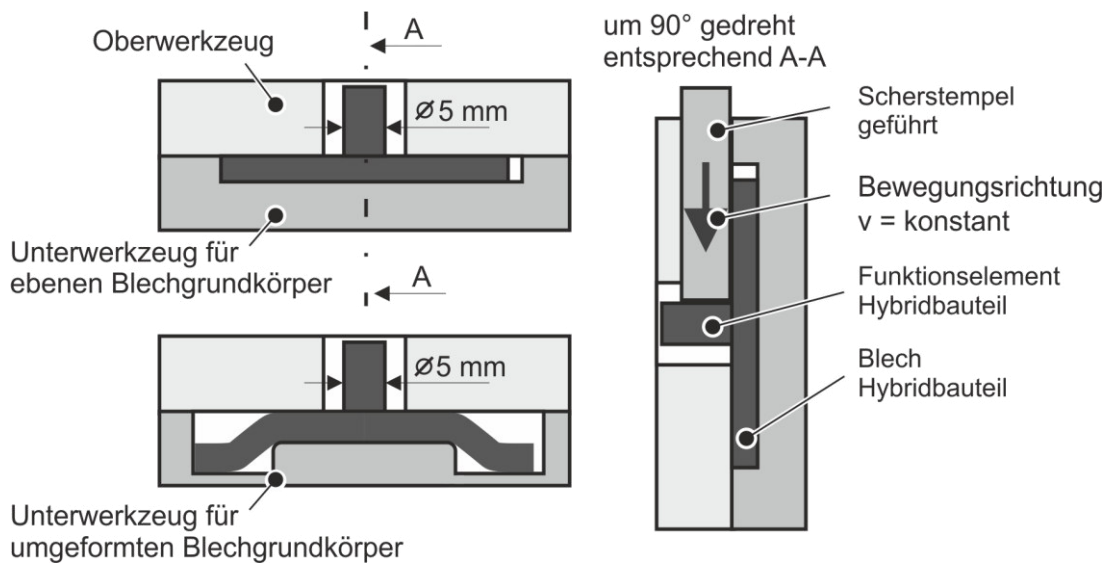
Schematischer Aufbau des Scherversuchs zur Bestimmung der Scherfestigkeit von hybrid gefertigten Bauteilen der Titanlegierung Ti-6Al-4V (a) mit Blickrichtung seitlich auf das Werkzeug und (b) mit Blickrichtung von oben
